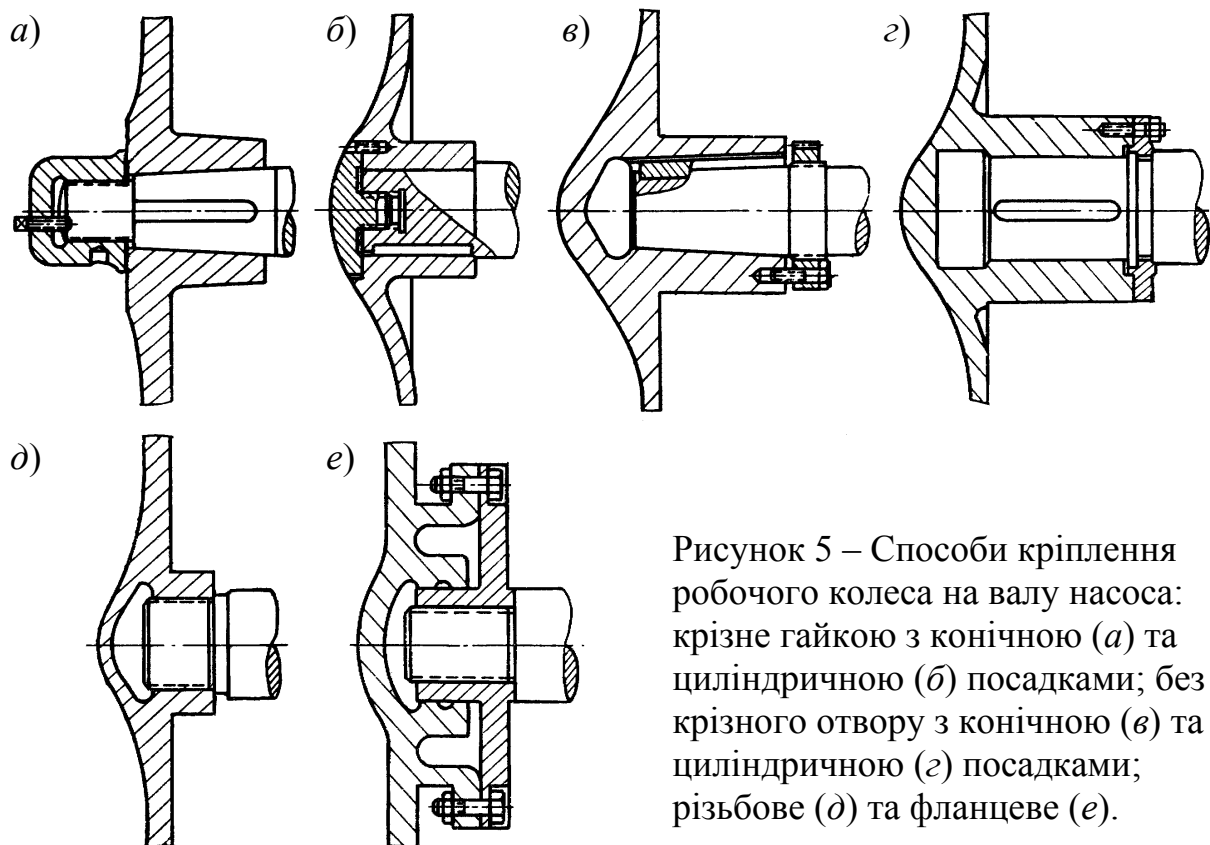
Способи кріплення робочого колеса на валу насоса: крізне гайкою з конічною (а) та циліндричною (б) посадками; без крізного отвору з конічною (в) та циліндричною (г) посадками; різьбове (д) та фланцеве (е).
